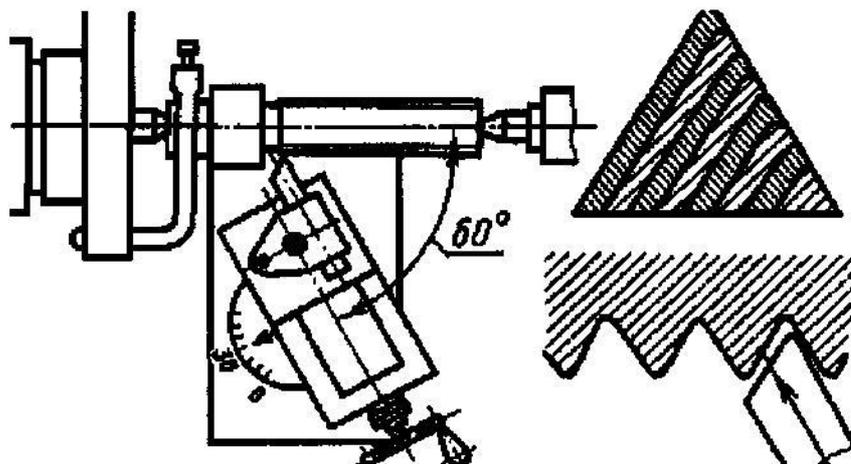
Схема работы резцонарезного резца при повернутых верхних салазках суппорта
